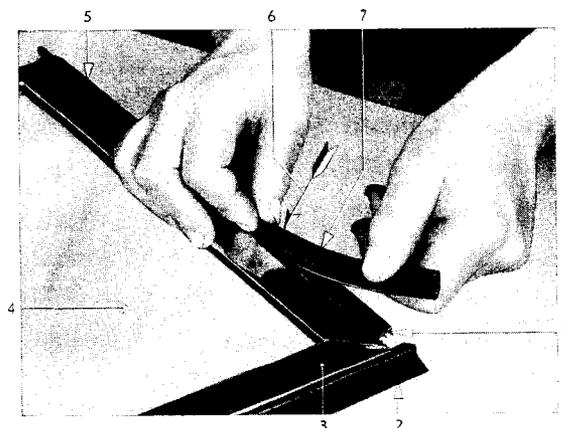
Kurze Gummiabdichtung auf Gelenkstück aufziehen
